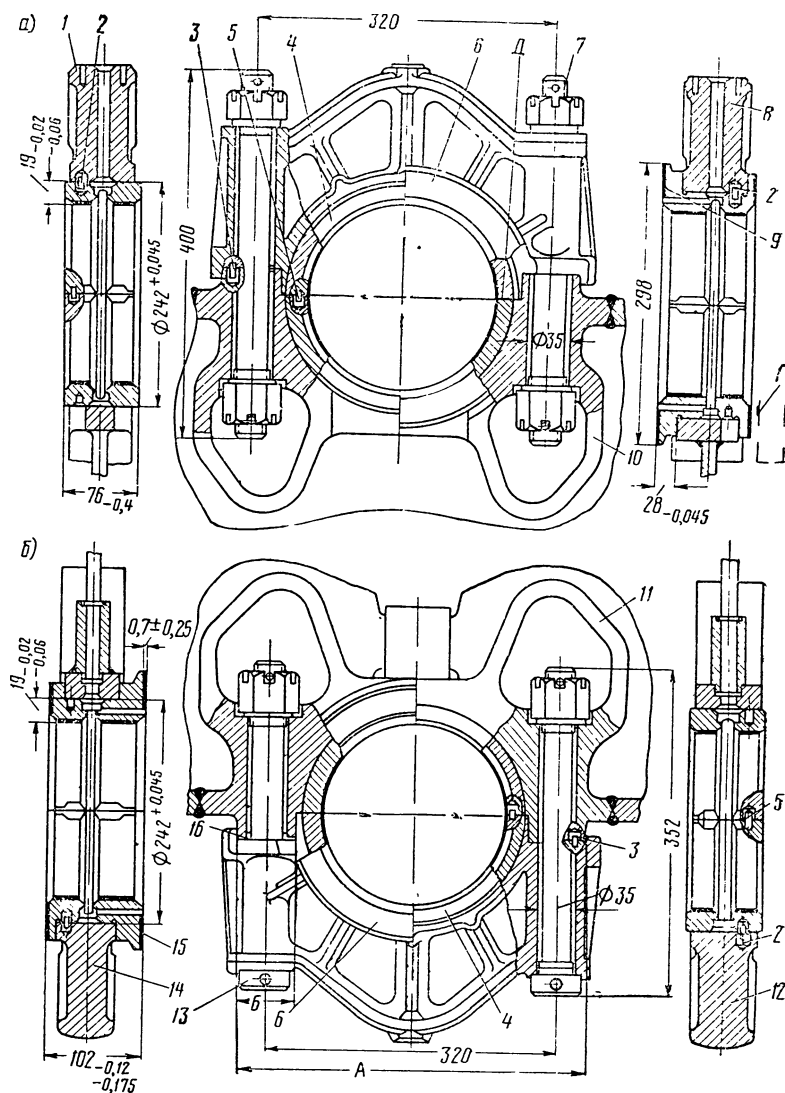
Коренные подшипники и крышки нижнего и верхнего коленчатых валов:
